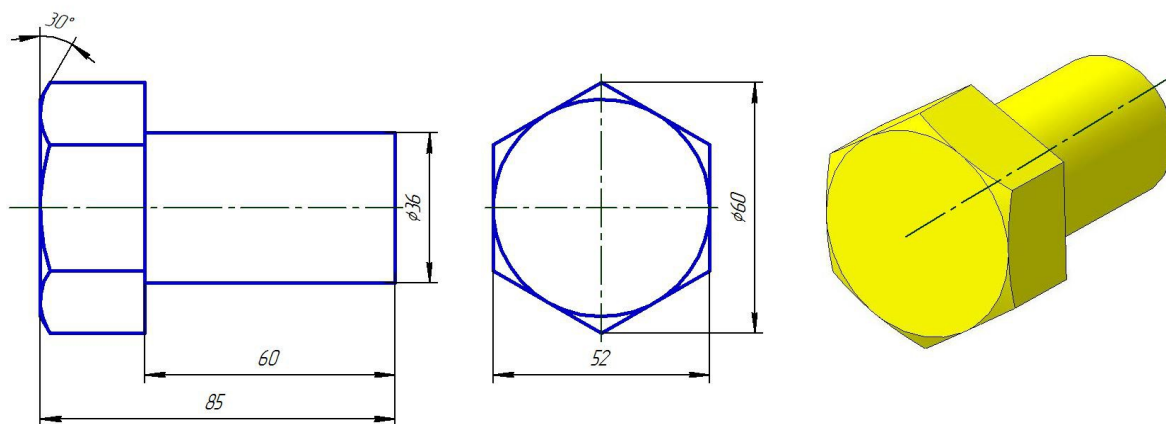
Чертеж и модель заготовки детали «Пробка»
